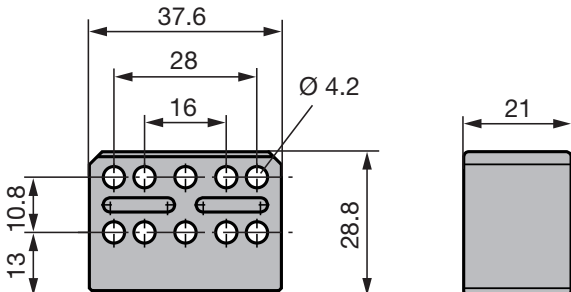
Medidas de montaje del sensor de posición BTL6-A-3800-2
